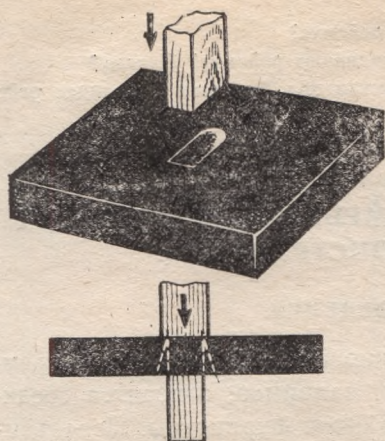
Пробивка брусочков через калибровочное отверстие.
